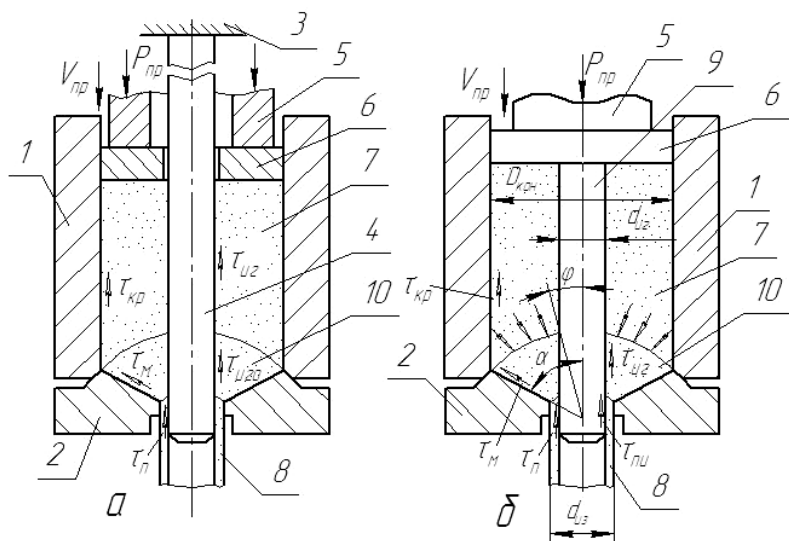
Прессование труб из полой заготовки с неподвижной (а) и подвижной (б) иглой: 1 – контейнер; 2 – матрица; 3 – неподвижный иглодержатель; 4 – неподвижная игла; 5 – пресс-штемпель; 6 – пресс-шайба; 7 – заготовка; 8 – труба; 9 – подвижная игла; 10 – очаг пластической деформации (ОПД);  $\tau_{кр}$  – напряжения трения по контейнеру,  $\tau_m$  – по матрице,  $\tau_n$  – по калибрующему пояску,  $\tau_{иг}$  – по телу иглы,  $\tau_{игОПД}$  – по телу иглы в зоне ОПД,  $\tau_{ни}$  – по игле в зоне пояска матрицы.
